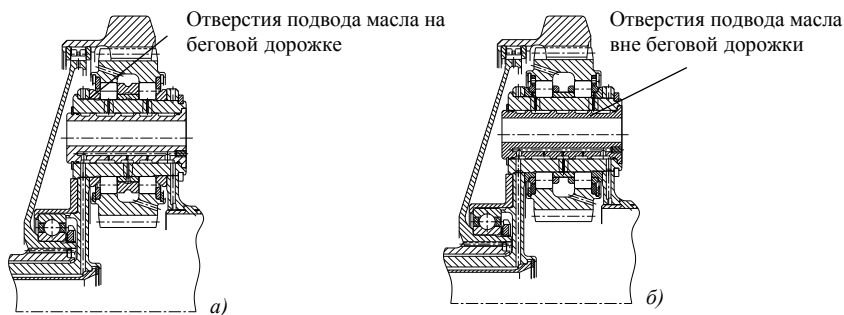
Схема подвода смазки в подшипники главного редуктора двигателя ТВЗ-117ВМА-СБМ1: а) исходная конструкция; б) доработанная конструкция подшипника сателлита
